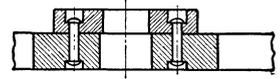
Schnittplatte auf der Grundplatte vernietet.
